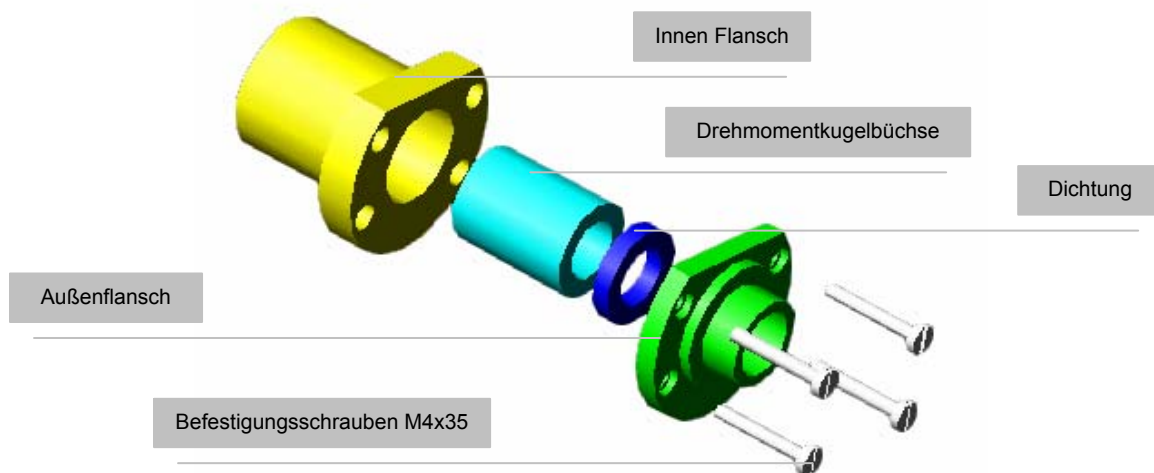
Flansche, Drehmomentkugelbüchse, Dichtung und Schrauben
